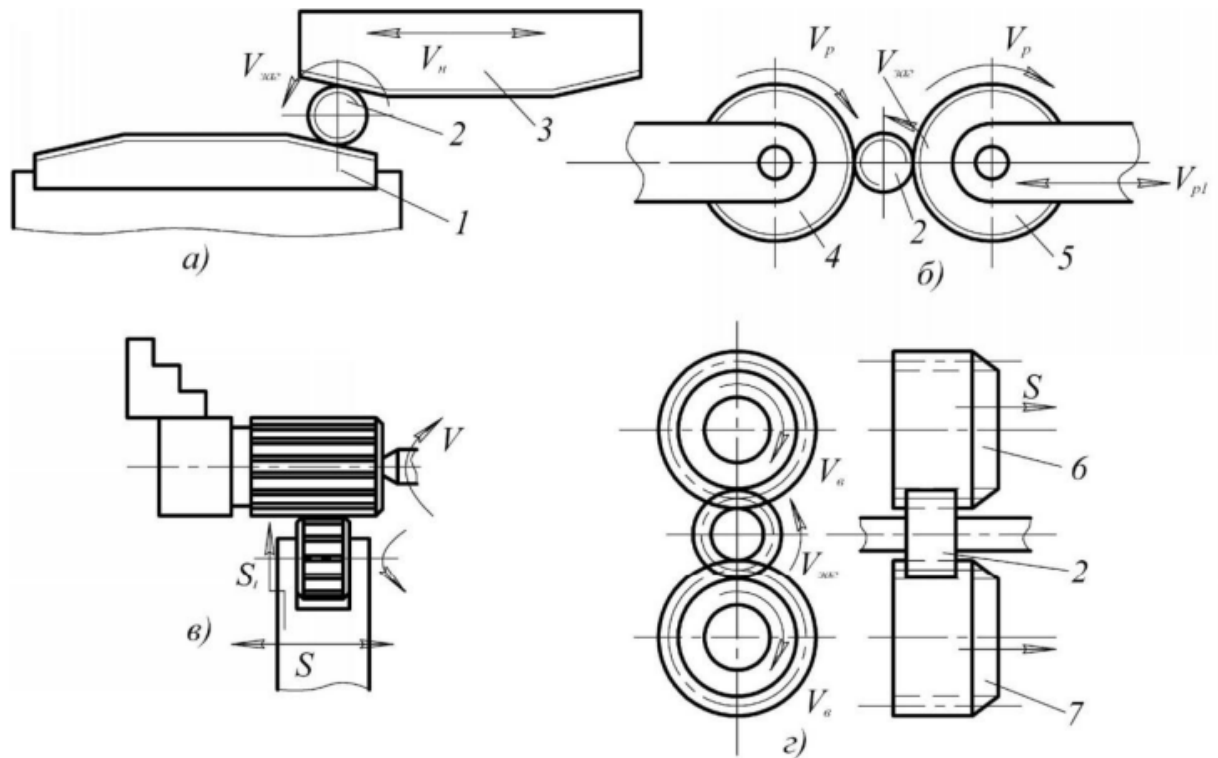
Схеми формоутворювальних методів обробки пластичним деформуванням
